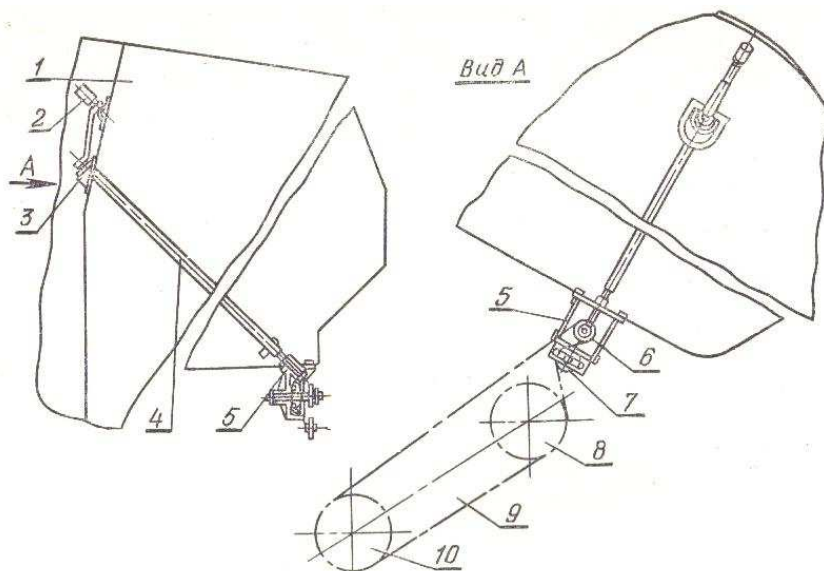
Механизм дистанционного управления частотой вращения барабана комбайна СК-6: 1 – бункер; 2 – ручка фиксатором; 3 – фланец; 4 – трубчатый вал; 5 – конический редуктор; 6, 7, 8, 10 – звездочки, 9 – цепь
